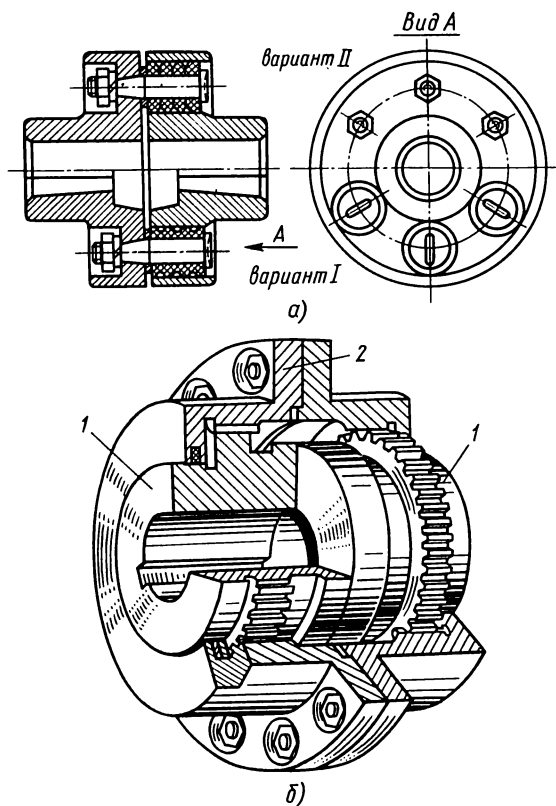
Муфта втулочно-пальцевая (а) и зубчатая (б)
